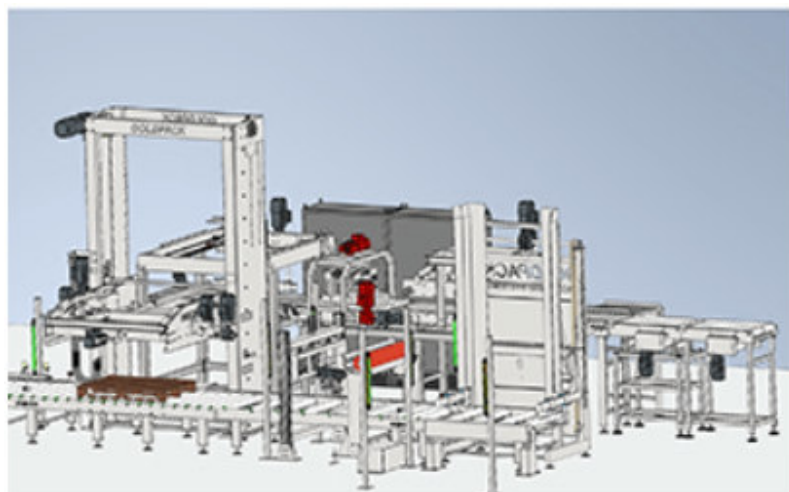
Автоматичний палетайзер PAL 1100
